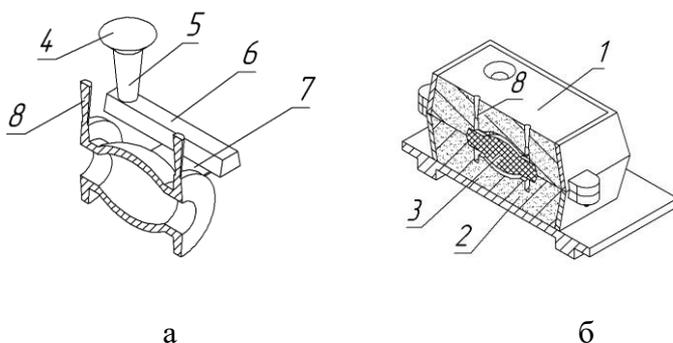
Отливка «Втулка» и литейная форма для ее изготовления
